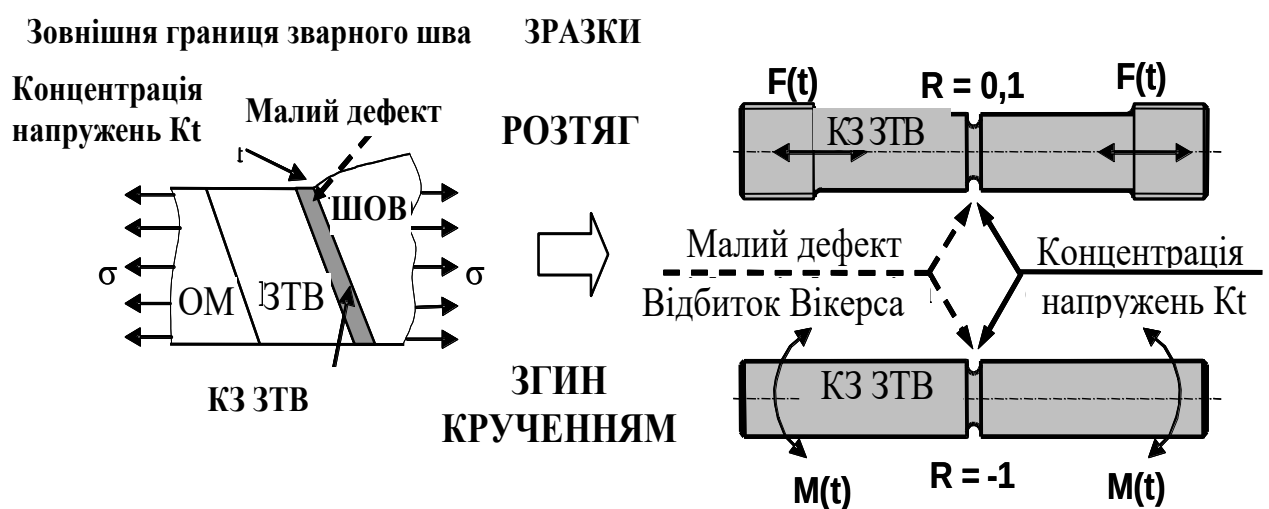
Форма стикового зварного з'єднання і умови на зовнішній границі зварного шва у двох зразках для випробування на втому крупного зерна ЗТВ
